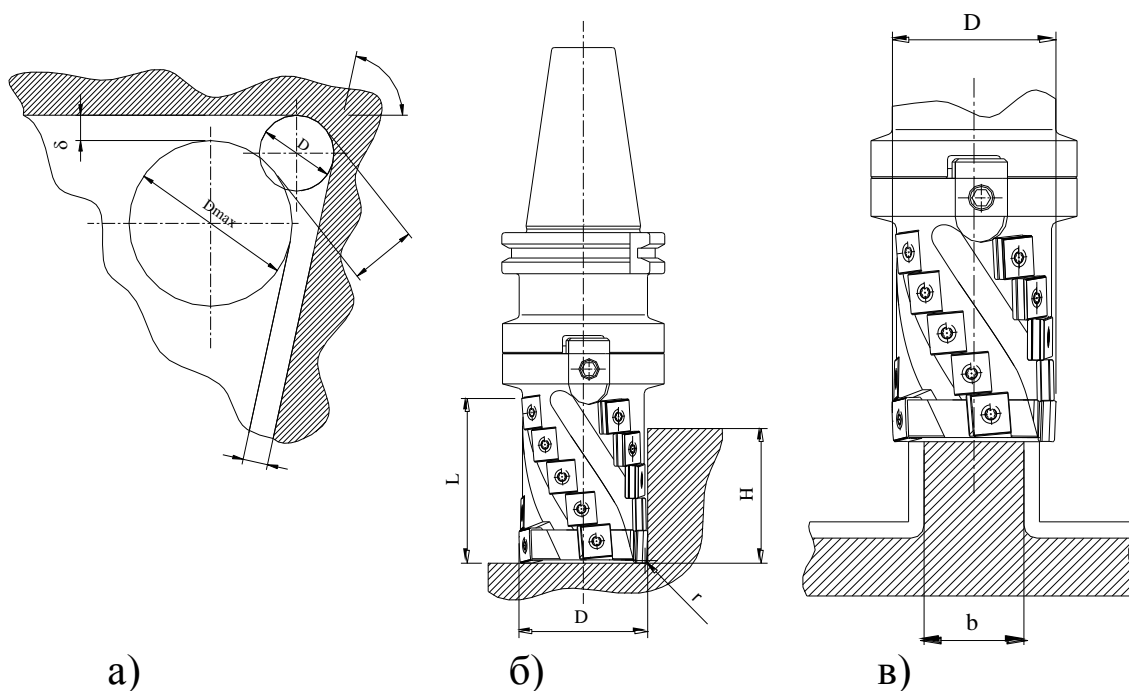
Схемы процессов обработки при выборе параметров фрезы
